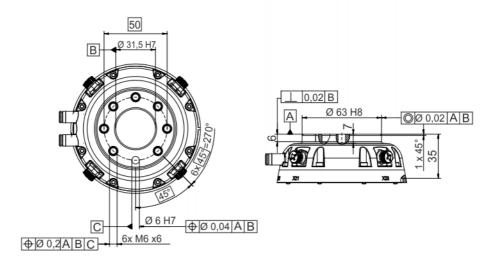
Abmessung, Medien-Flansch pneumatisch
